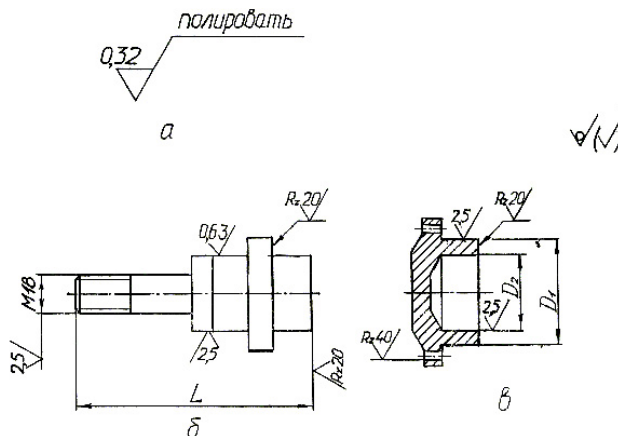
Примеры оформления чертежа с обозначением шероховатости
